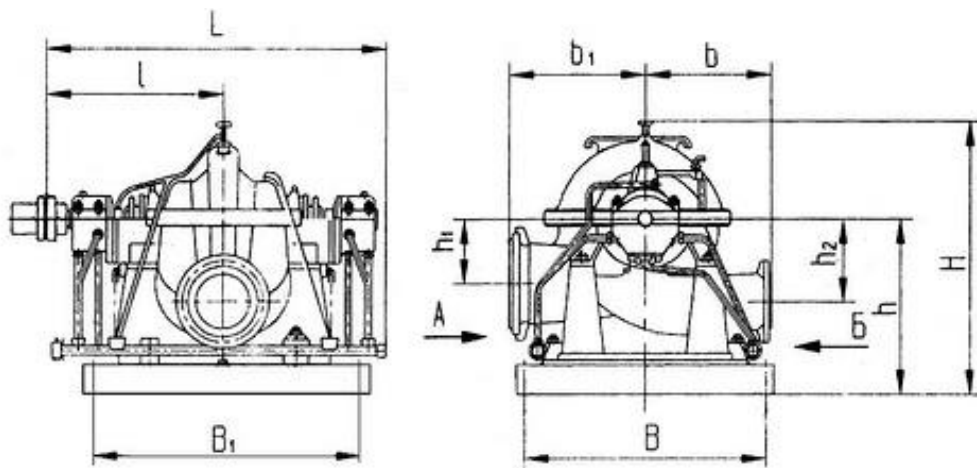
Габаритный чертёж сетевого насоса СЭ-1250-70-11
